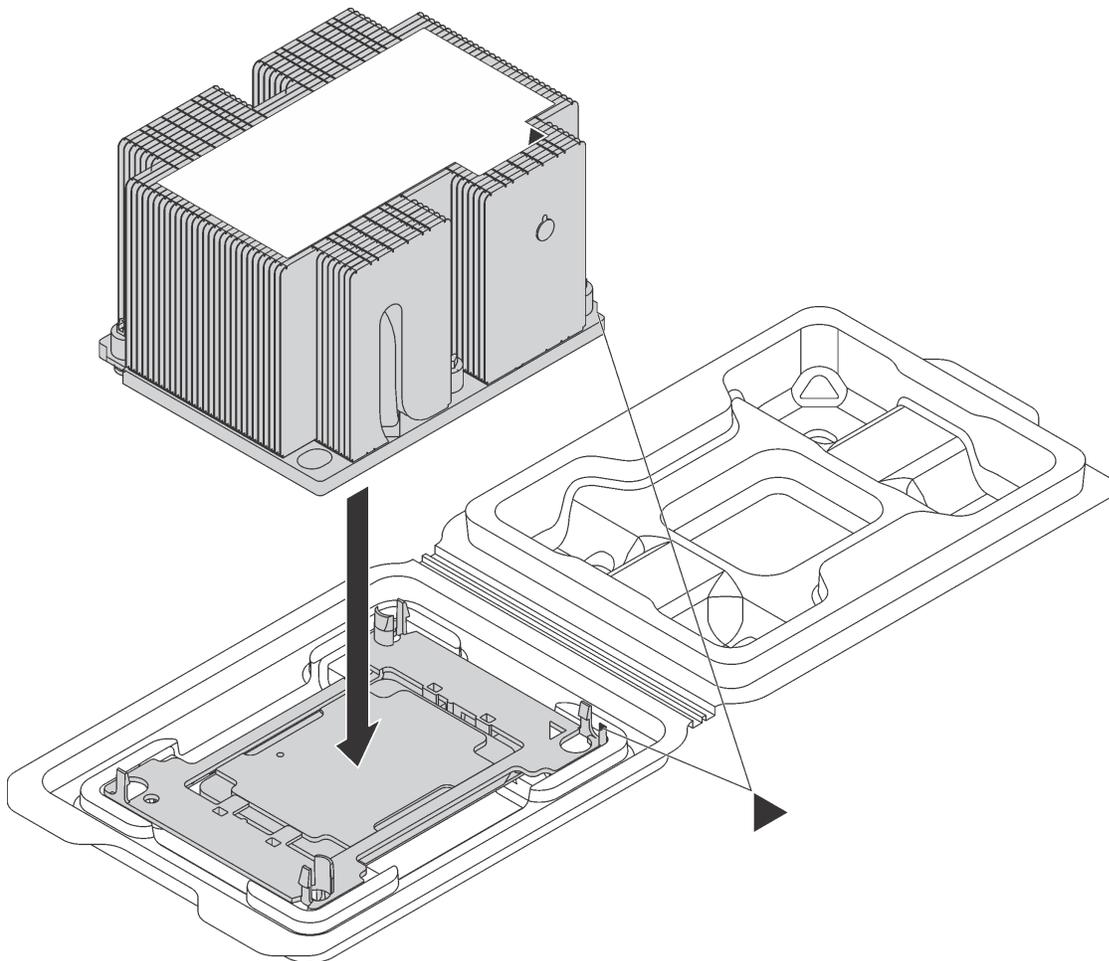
Assembler un module de processeur-dissipateur thermique dans le bac de transport
